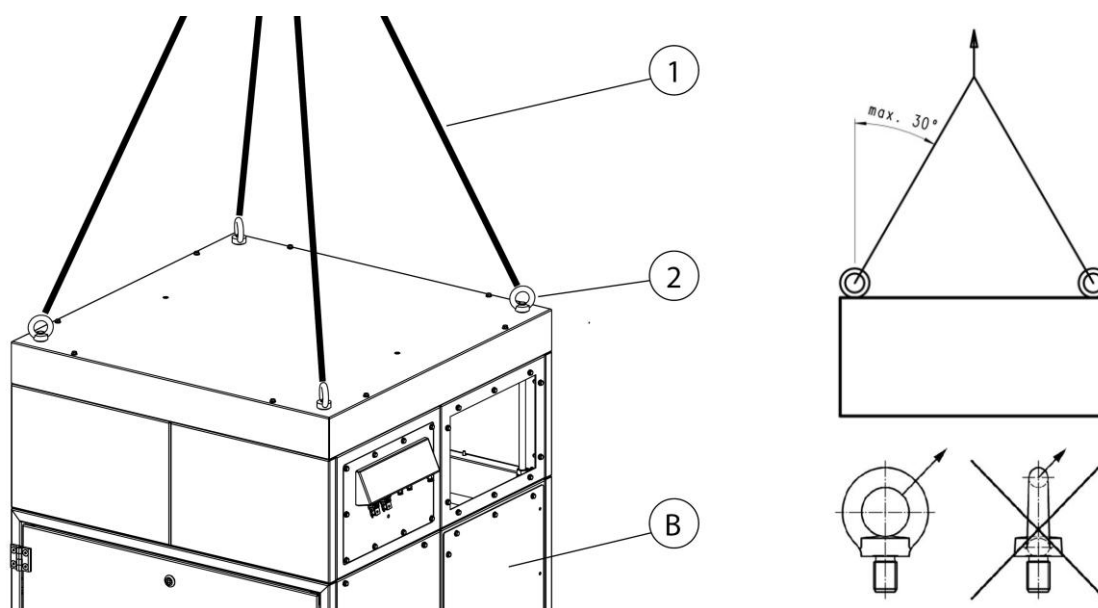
Elevar el producto con grúa/ equipo de elevación
